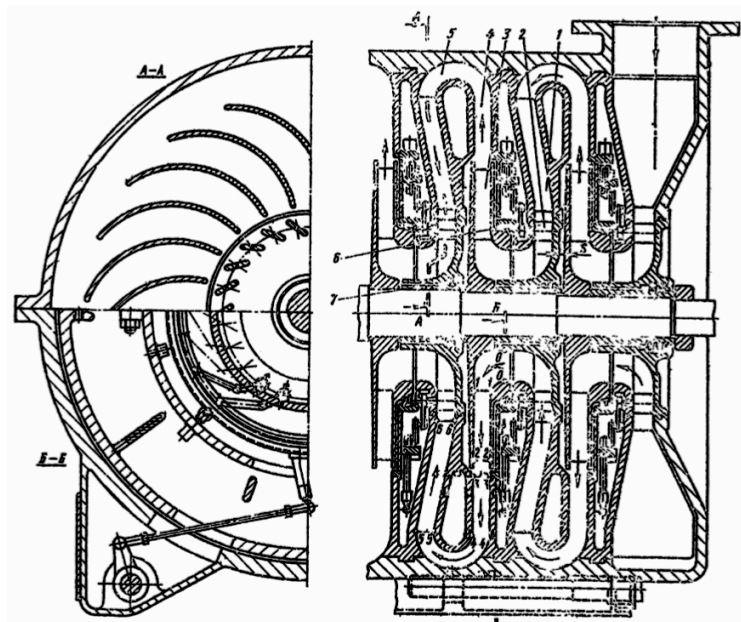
Схема конструкции трехступенчатого центробежного компрессора
